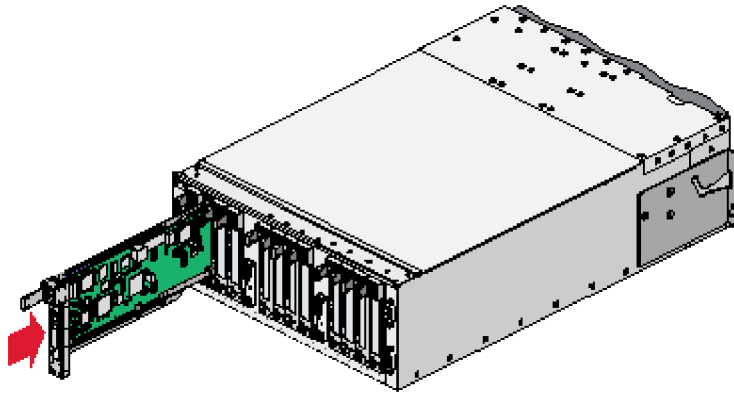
Déplacement de la barre de guidage du support pour fixer la carte PCI demi-hauteur
